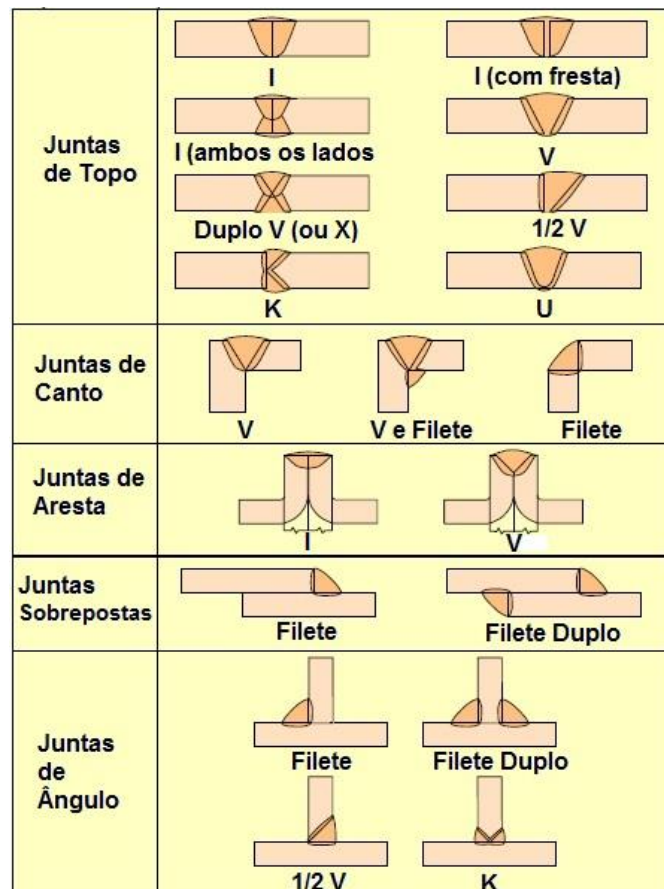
Principais tipos de juntas e chanfros utilizados na soldagem [Bracarense et al., 2005].
